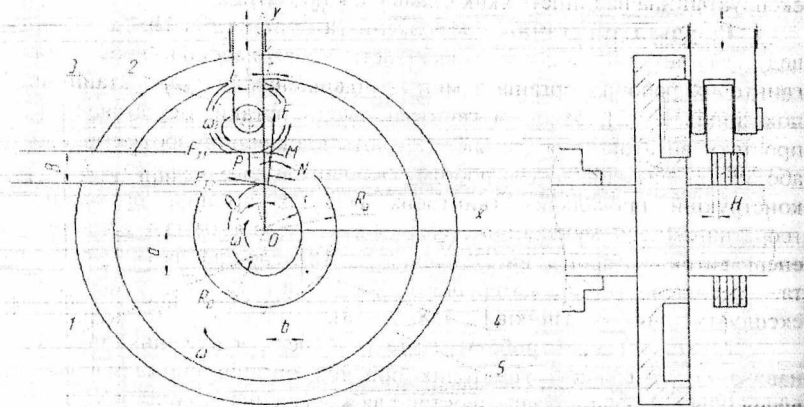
Розрахункова схема процесу навивання гвинтового робочого органу сільхозмашин на оправу: 1 - еліпсна оправка; 2 - притискний ролик; 3 - стрічка; 4 - гвинтовий еліпсний елемент; 5 - торцевий кулачок, форма якого відповідає еквідистанті еліпсної оправки 1
